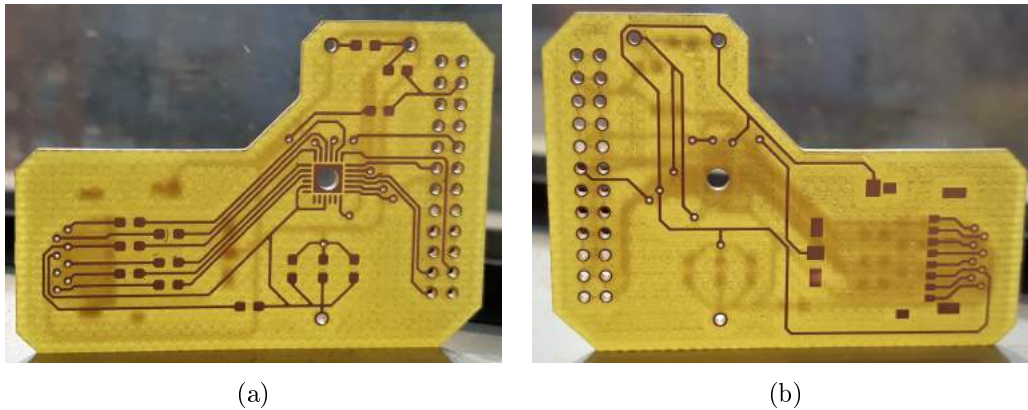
Vista frontale dello strato superiore (a) ed inferiore (b) della PCB appena terminata la fase di fresatura, pronta per la saldatura dei componenti.
